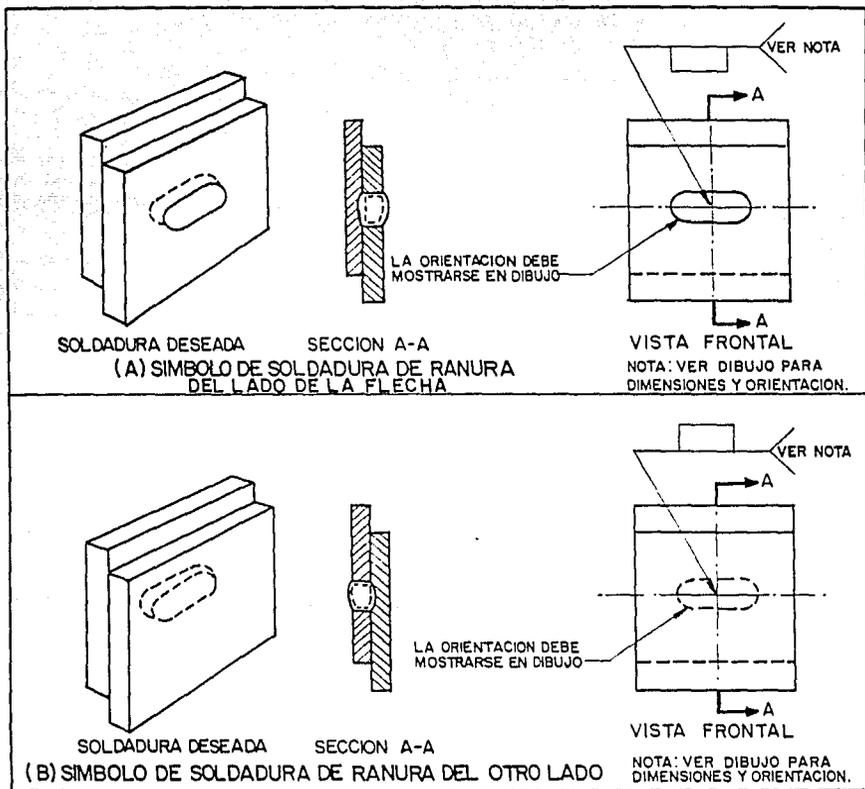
APLICACION DEL SIMBOLO DE SOLDADURA DE RANURA
